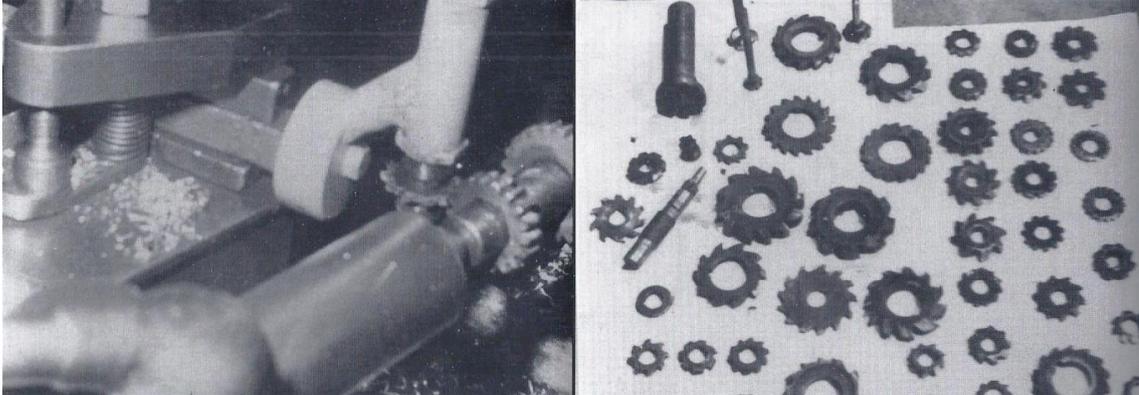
A la izquierda, el sistema para creación de engranajes adaptado a torno convencional diseñado por Augusto Cicaré. A la derecha, algunos engranajes y ruedas dentadas creadas con la máquina (1954).
